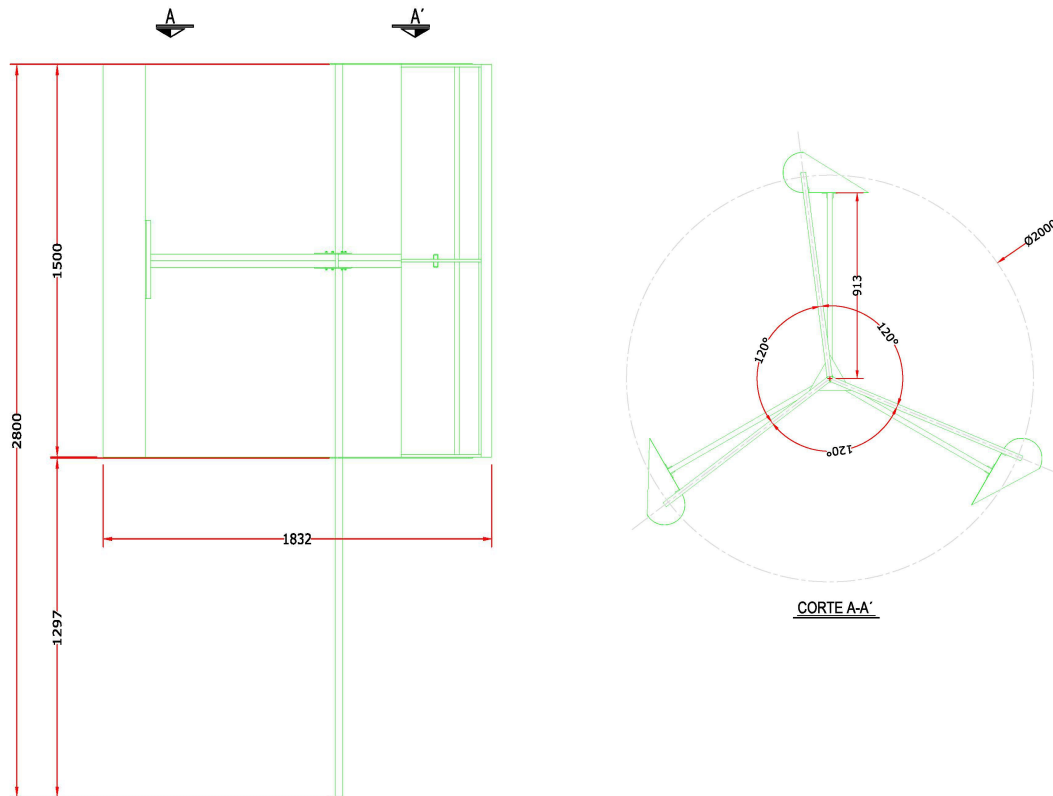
Dimensiones de prototipo LENZ, Dimensiones en mm.
